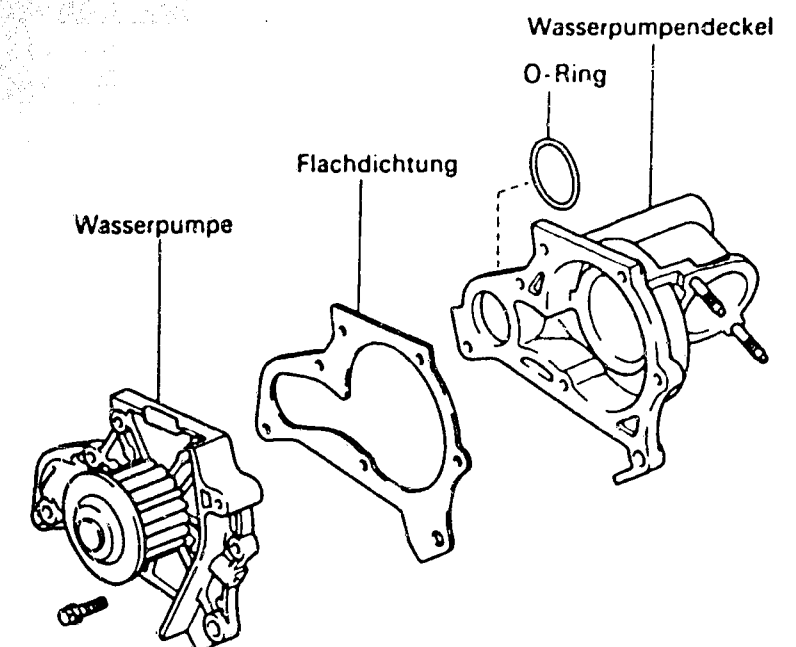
Motoren 3S-GE und 1S: Aus- und Einbau der Wasserpumpe von der Stirnradseite her. Die Schrauben sind beim Einbau in der gezeigten Reihenfolge mit 7,8 Nm festzuziehen.
